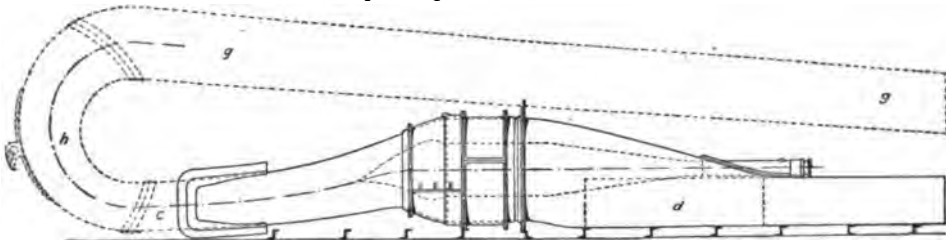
Längsschnitt mit Ansicht einer Turbine.
